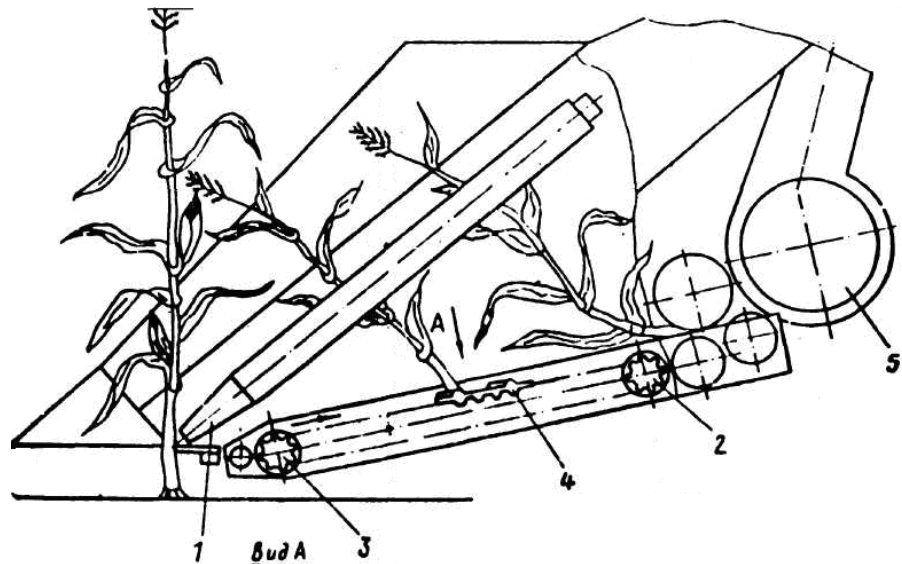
Схема жатки оснащеної подавальним механізмом елеваторного виду: 1-качановідривний механізм; 2- привідний вал; 3- вал ведений; 4-елеватор; 5-камера подрібнення
